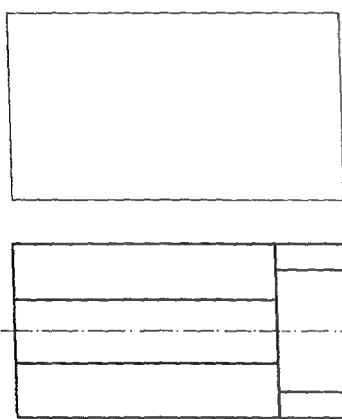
Dibujar el alzado del objeto del que se dan planta y perfil.
